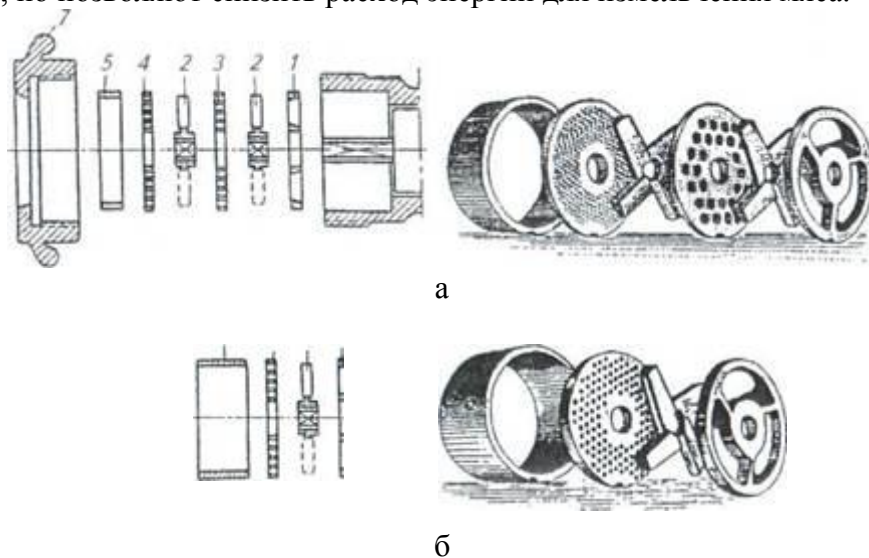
Схемы сборки режущего механизма волчка:
